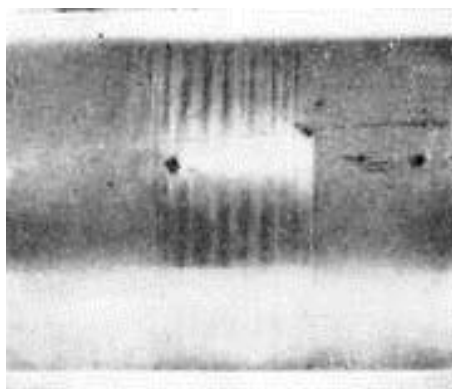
Шероховатые локальные неглубокие риски от обработки резанием
